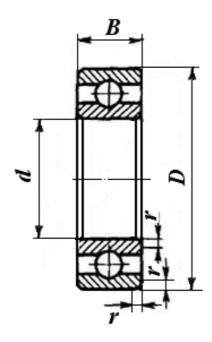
Основные размеры подшипника шарикового радиального однорядного
